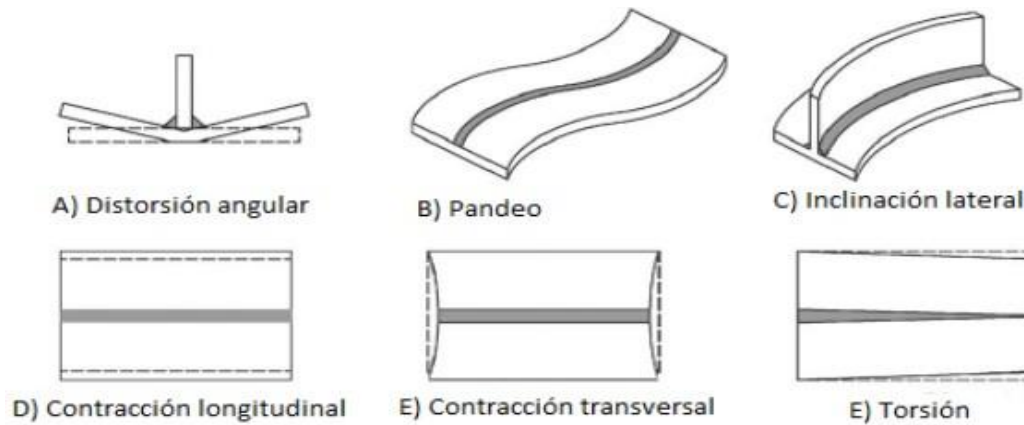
Tipos por Distorsión por Soldadura [19].
